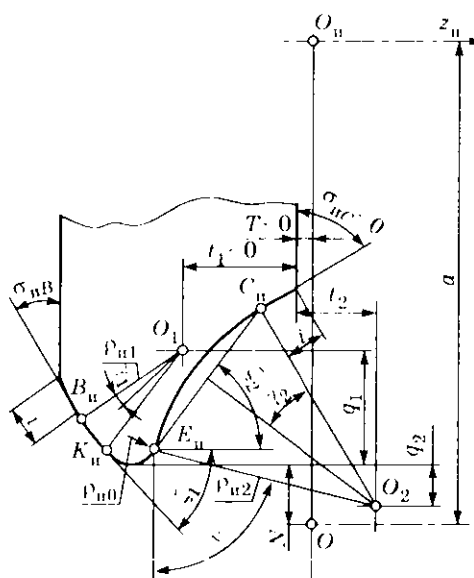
Схема замены точного профиля дисковой фасонной фрезы для обработки канавки фрезы с параболическим зубом дугами окружностей
